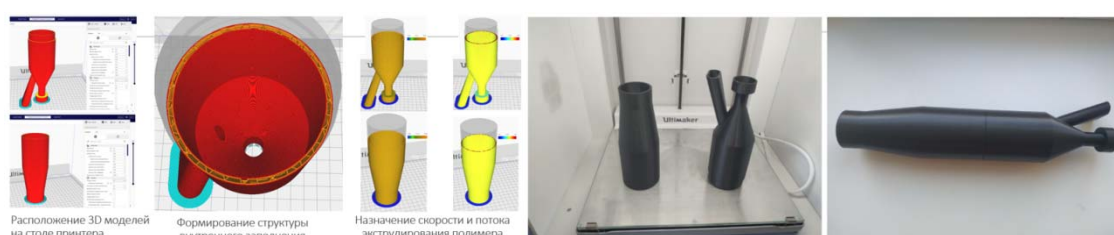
Подготовка оптимизированного изделия к 3D-печати и реальный образец
